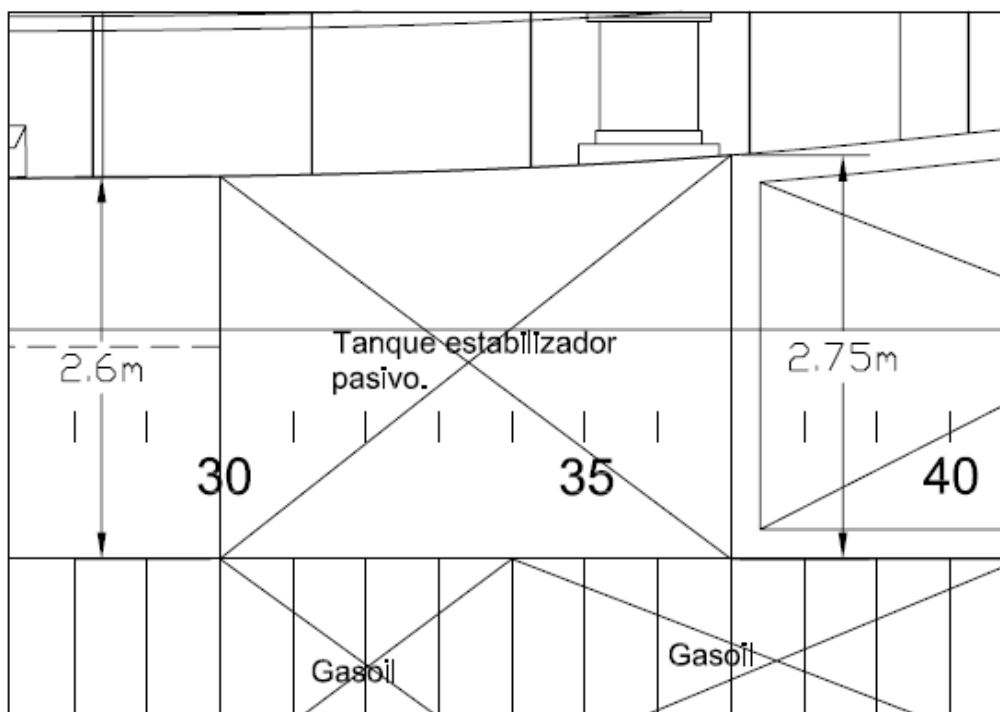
Perfil del espacio destinado al tanque estabilizador.
